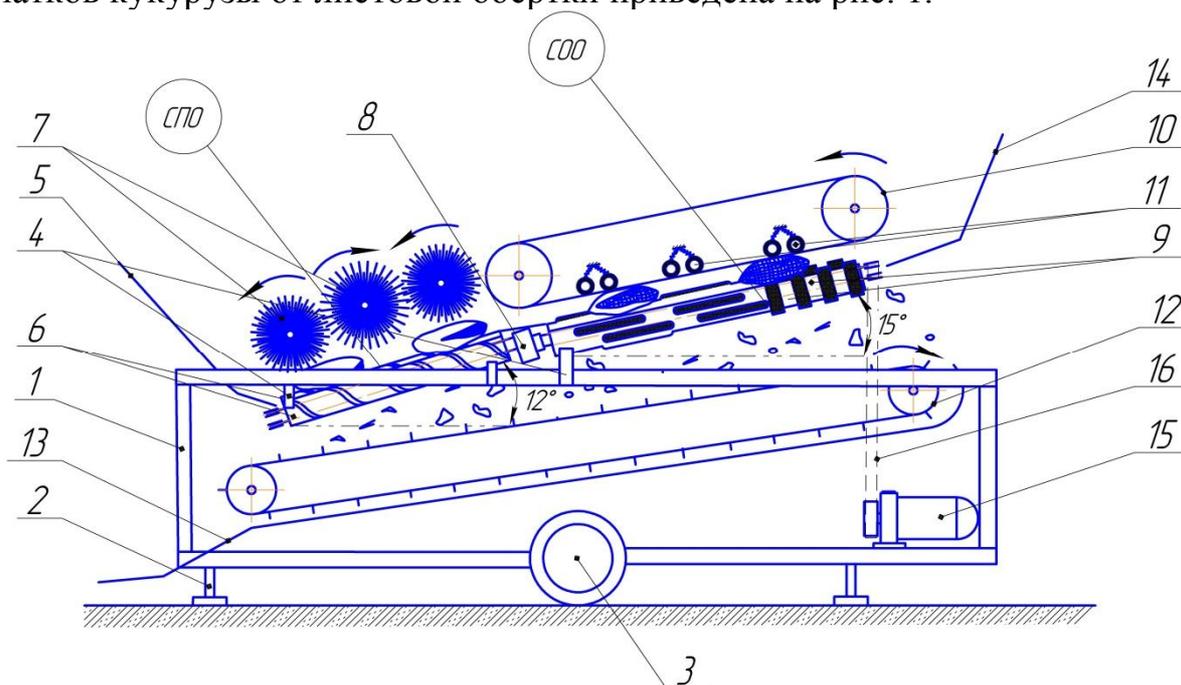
Двухступенчатый очиститель початков кукурузы от листовой обёртки: СПО – ступень предварительной очистки; СОО – ступень основной очистки; 1-рама; 2-опорная стойка; 3-колесо; 4-механизмы регулировки угла наклона валцов; 5-загрузочный лоток; 6- валцы предварительной очистки; 7-обёрткорассекающие барабаны; 8-редуктор; 9- валцы основной очистки; 10-транспортёрное прижимное устройство; 11-ролики распределители; 12-транспортёр обёрток; 13-выгрузной лоток для обёрток; 14-выгрузной лоток для початков; 15-электродвигатель; 16-передача.
